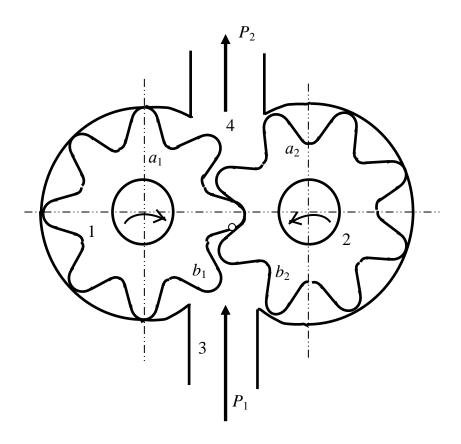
Схема работы двухшестеренного насоса с внешним зацеплением: 1, 2 — шестерни; 3 — камера всасывания; 4 — камера нагнетания
